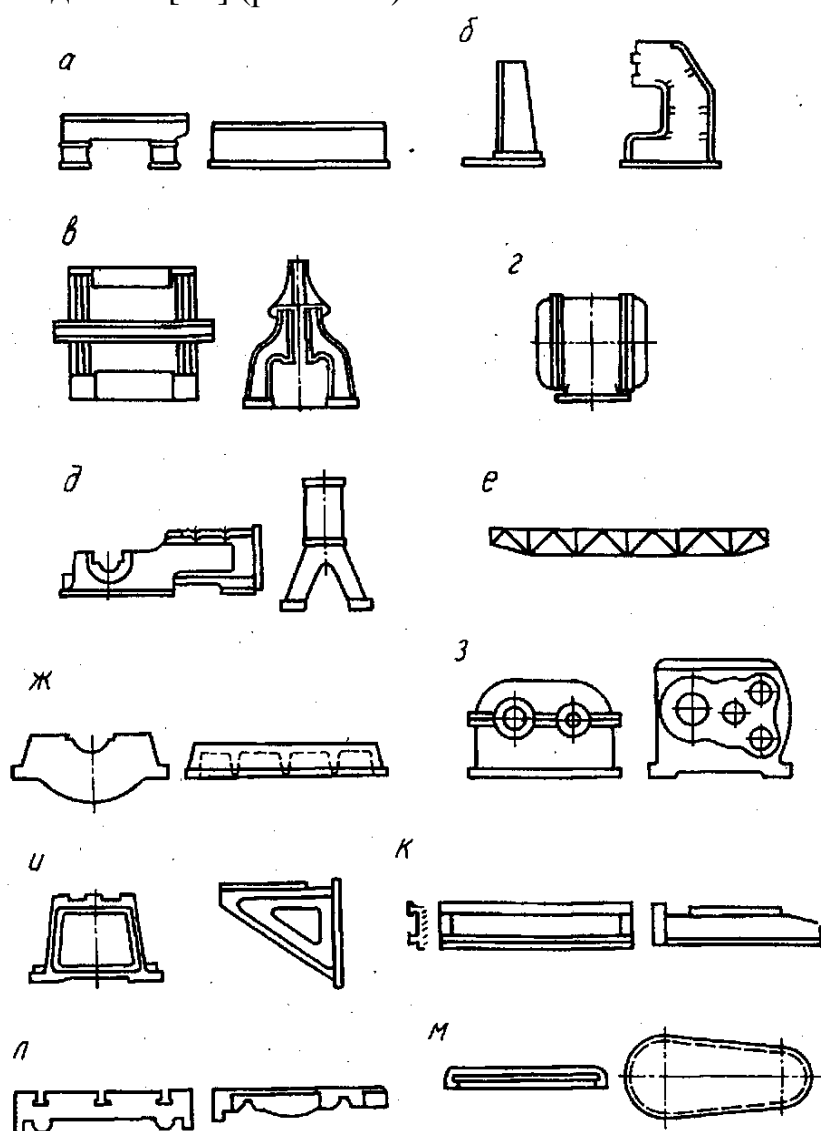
Корпусные детали: *а* – станины горизонтальные; *б* – станины вертикальные; *в* – станины порталные; *г* – станины кольцевые; *д* – блоки цилиндров; *е* – рамы; *ж* – основания, плиты; *з* – коробки; *и* – стойки, кронштейны; *к* – поперечены, ползуны; *л* – столы, салазки; *м* – крышки, кожухи
